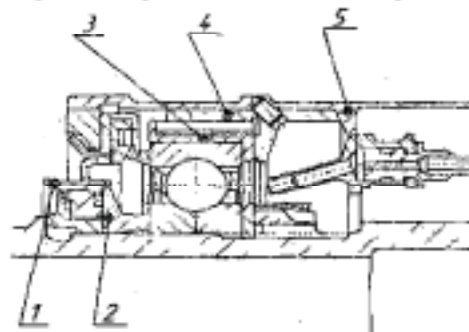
Конструкция РУП ротора НД: 1-втулка; 2-регулирующее кольцо; 3-внутреннее кольцо демпфера; 4-втулка; 5-корпус подшипника
